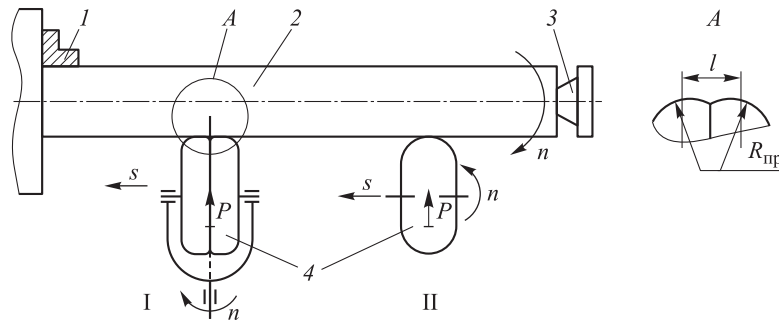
Схемы упрочняющей обработки двухрадиусным (I) и однорадиусным роликом (II) на токарном станке (а) и вид рабочей части двухрадиусного ролика (б): 1 — трехкулачковый патрон; 2 — заготовка; 3 — задняя бабка; 4 — инструмент
